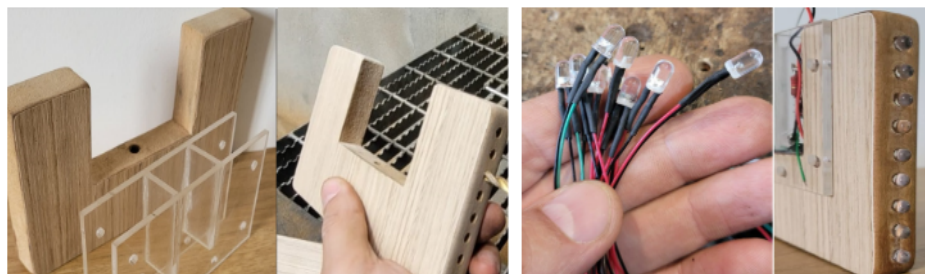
Estrutura do chassi rotativo e soldagem de leds.
